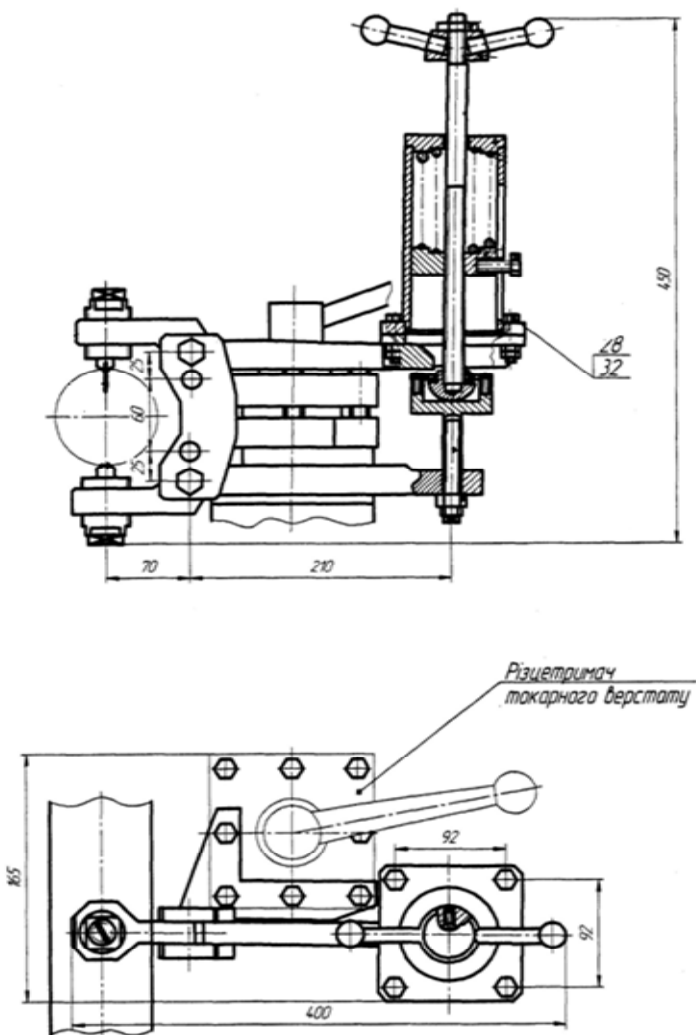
Пристрій для нанесення покриттів на зовнішні поверхні
